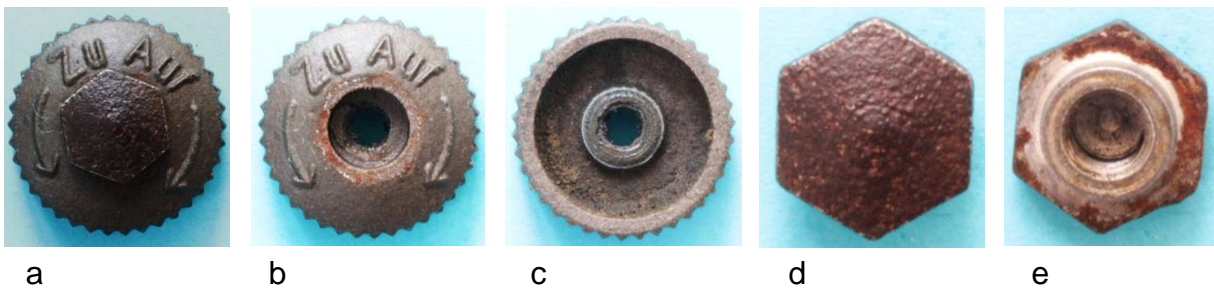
Reibrad: a) Reibrad mit Hutmutter, b) Reibrad mit Innengewinde, c) Unterseite, d) Schraubenkopf, e) Hutmutter mit Innengewinde
